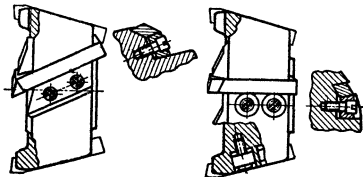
Messerköpfe mit geraden Messern und keilförmiger Befestigung.
